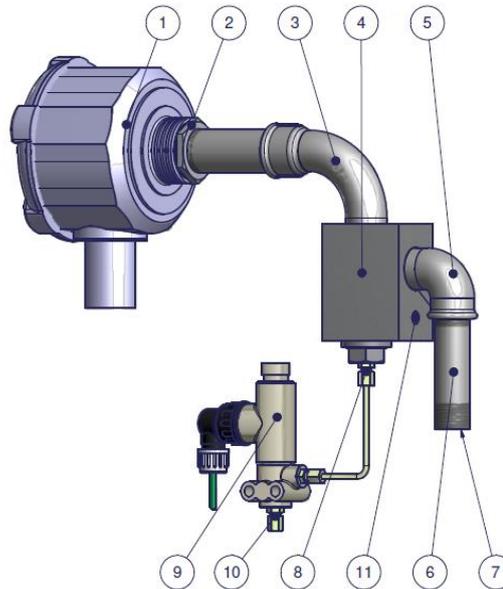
Aufbau Kompressor bzw. Vakuumpumpe
